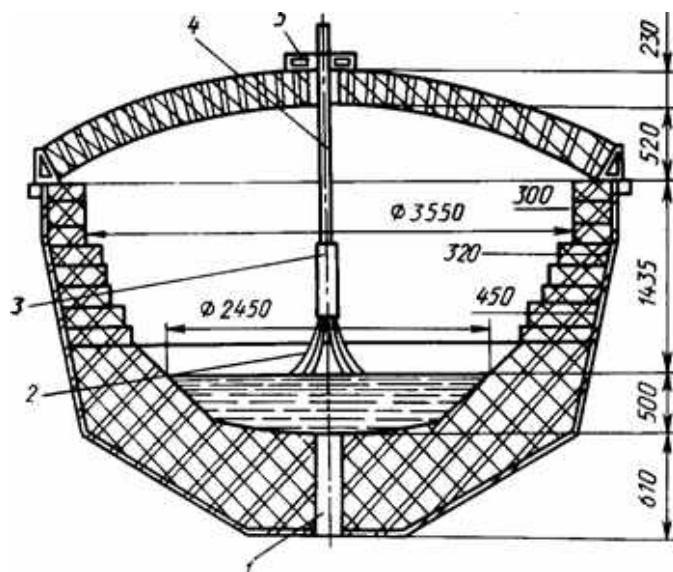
Футеровка дуговой печи постоянного тока
